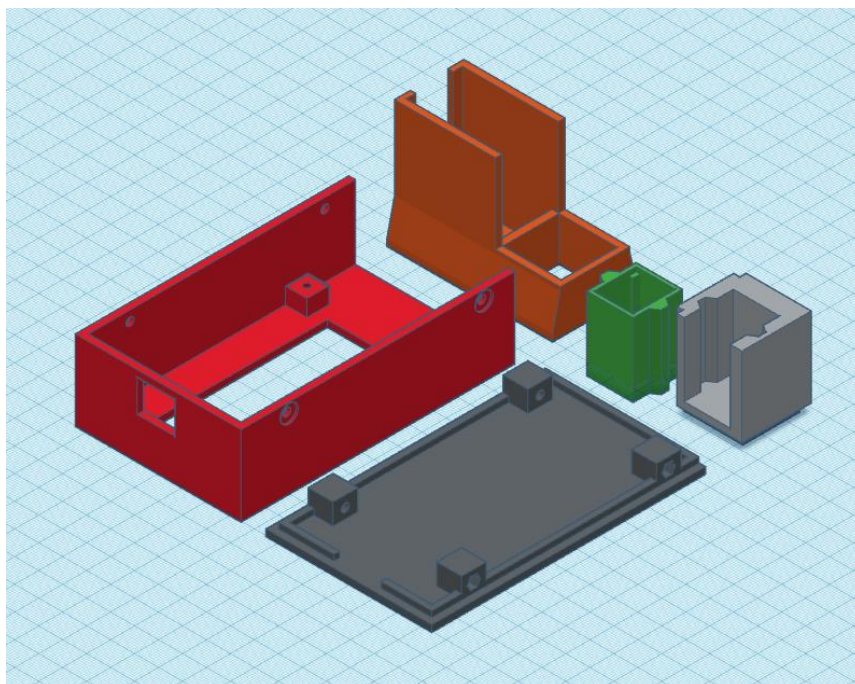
3D модель деталей корпусу Ethernet тестера.
